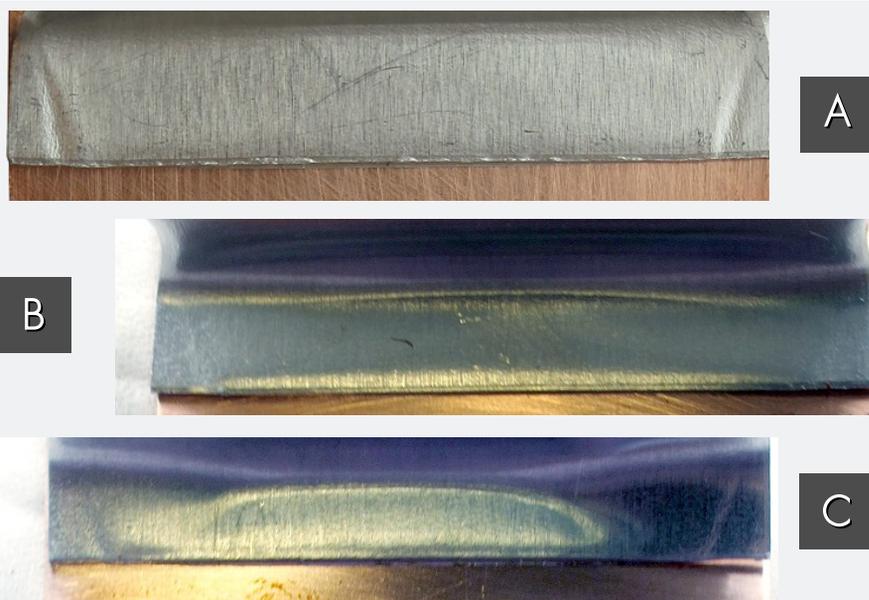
zone de soudage obtenue après test 'peel': (A) 18 kJ, (B) 16 kJ, (C) 14 kJ (source: Institut Belge de la Soudure)
